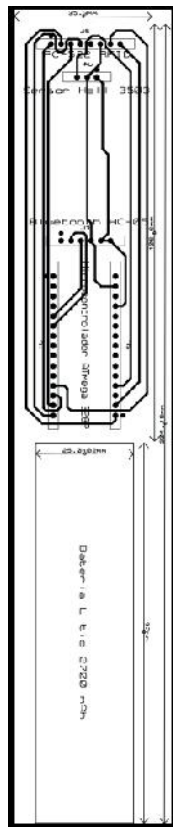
Diseño PCB (Fuente autores 2016) [3]
